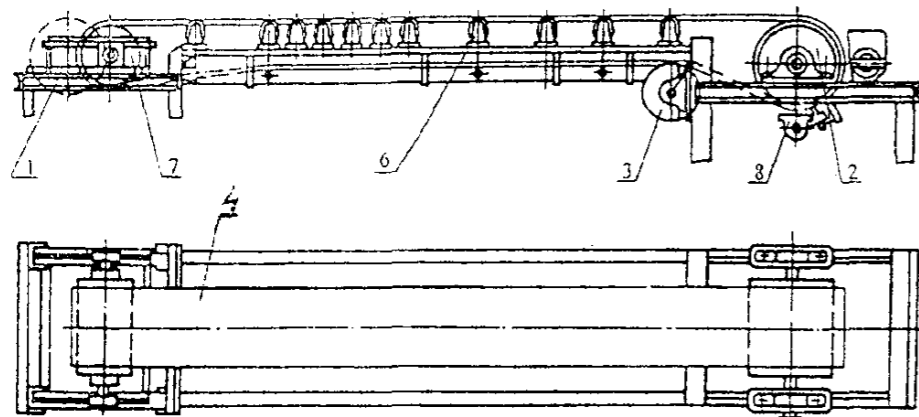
1-устройство натяжное; 2-барабан приводной; 3-барабан отклоняющий; 4-лента; 5-привод; 6-роликсопоры; 7-барабан концевой; 8-устройство ошестное
